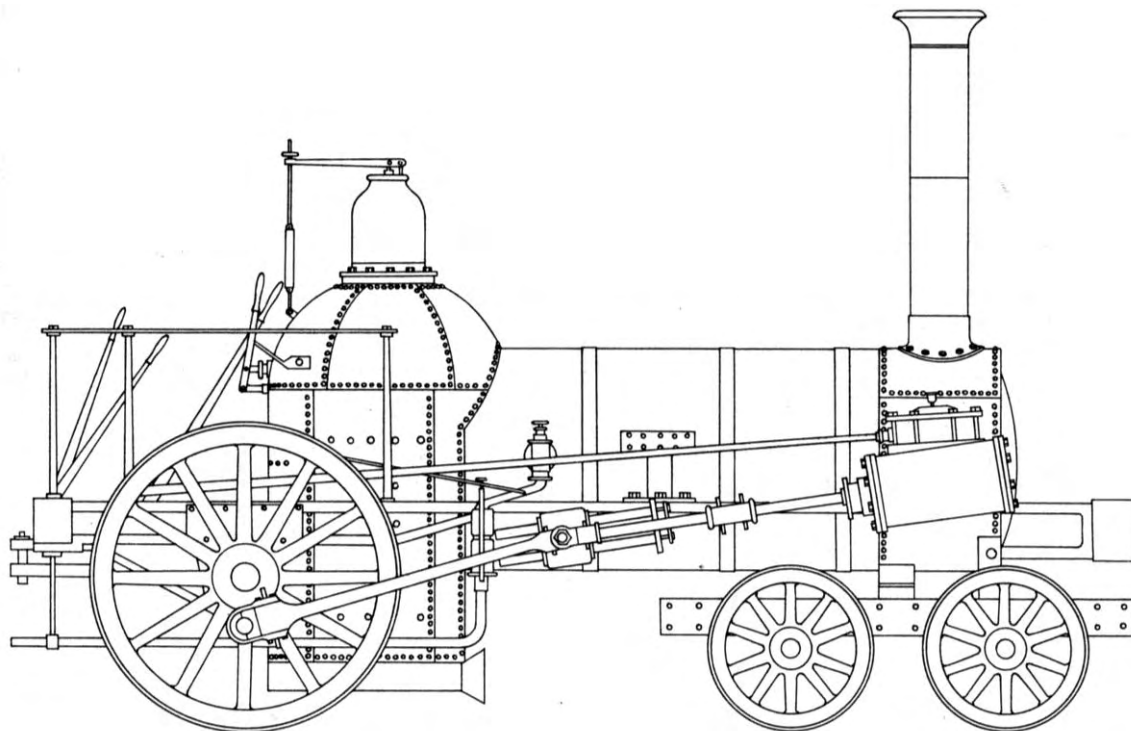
Fig. IV : " L'AIGLE NOIR ", première locomotive construite par Baldwin sur la base d'un " long boiler ".
